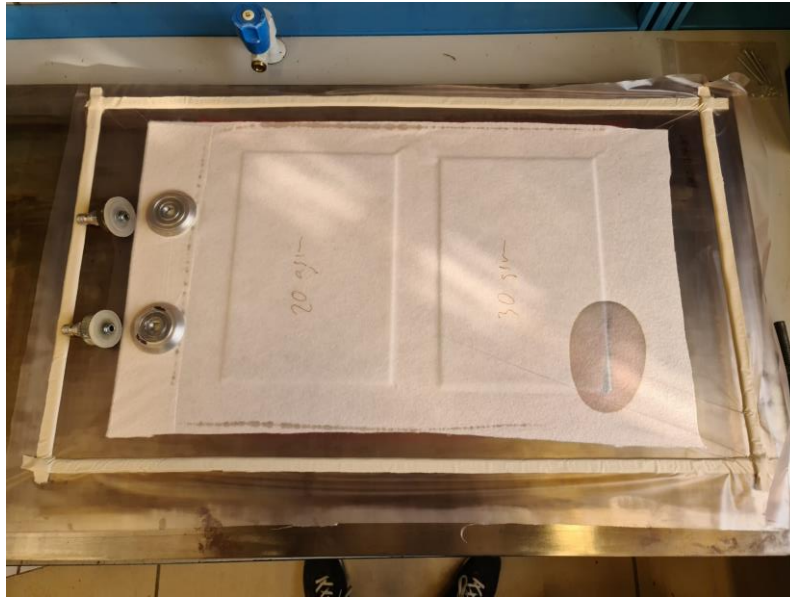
Plancha metálica con los laminados curados justo a la salida del autoclave.
